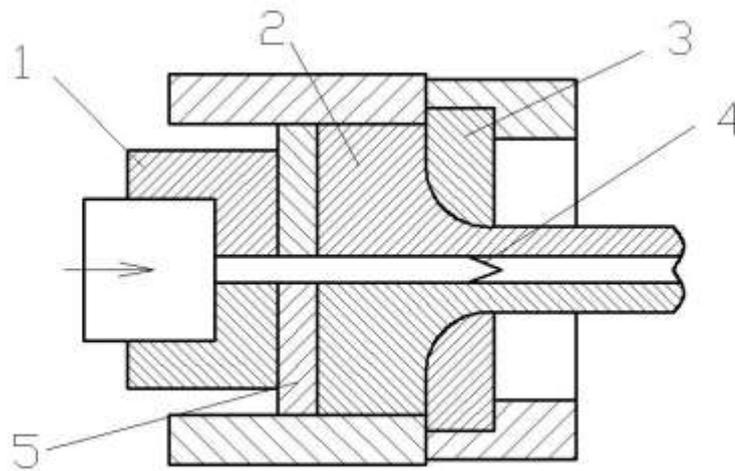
Схема прессования полого профиля. 1 – пуансон; 2 – металл заготовки; 3 – матрица; 4 – игла; 5 – пресс-шайба;
